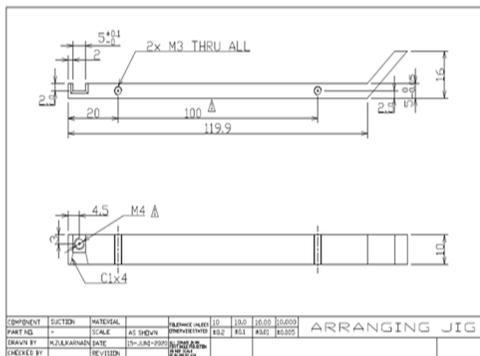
Production drawing JIG (Stick Frame bagian bawah)
